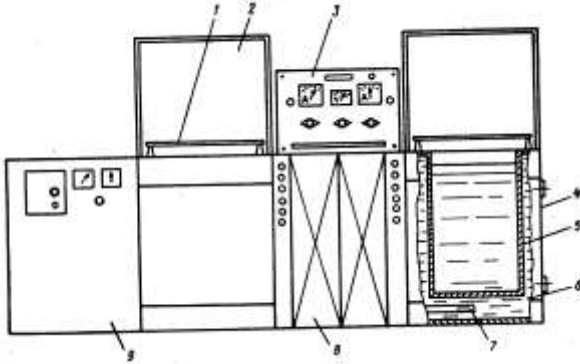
Установка для хромування деталей: 1 – штанги; 2 – кришка; 3 – пульт керування; 4 – корпус; 5 – внутрішня ванна; 6 – мінеральне масло; 7 – нагрівальний елемент; 8 – шафа з вентиляційною установкою; 9 – джерело живлення
